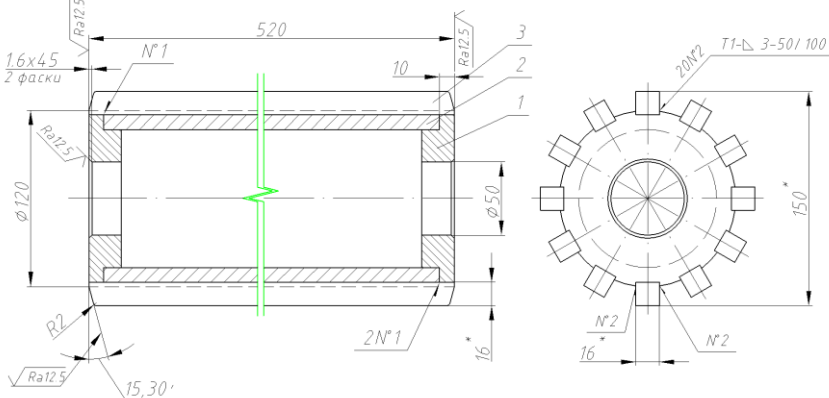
Конструкція барабана для подачі конвеєрної стрічки в зону різання: 1 – диски; 2 – втулка; 3 – шліци
